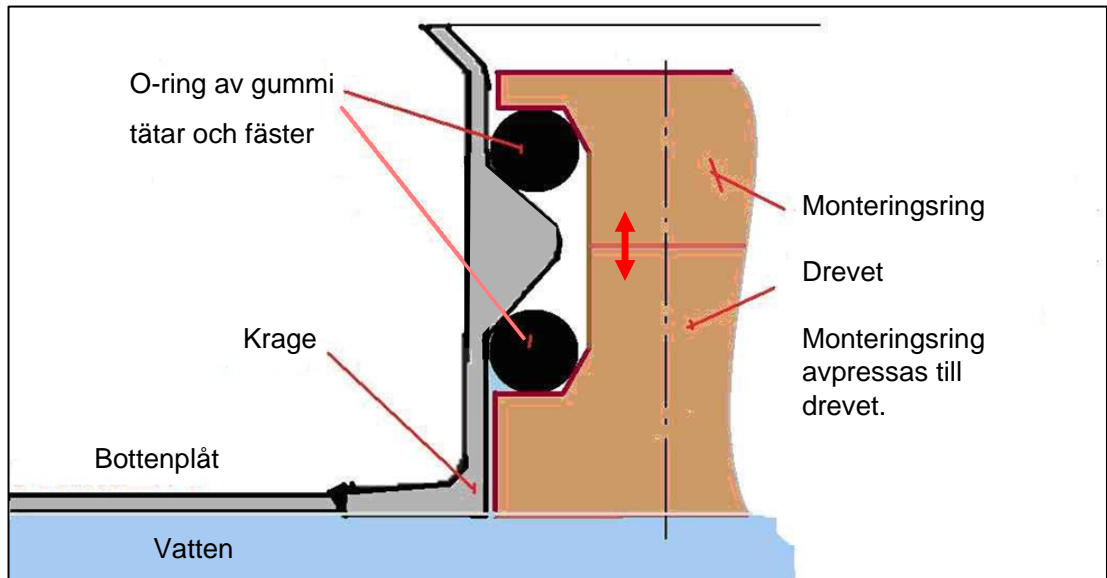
Drevets installation till skrovet genomförs med hjälp av en krage med två stora O-ringar och en monteringsring.
